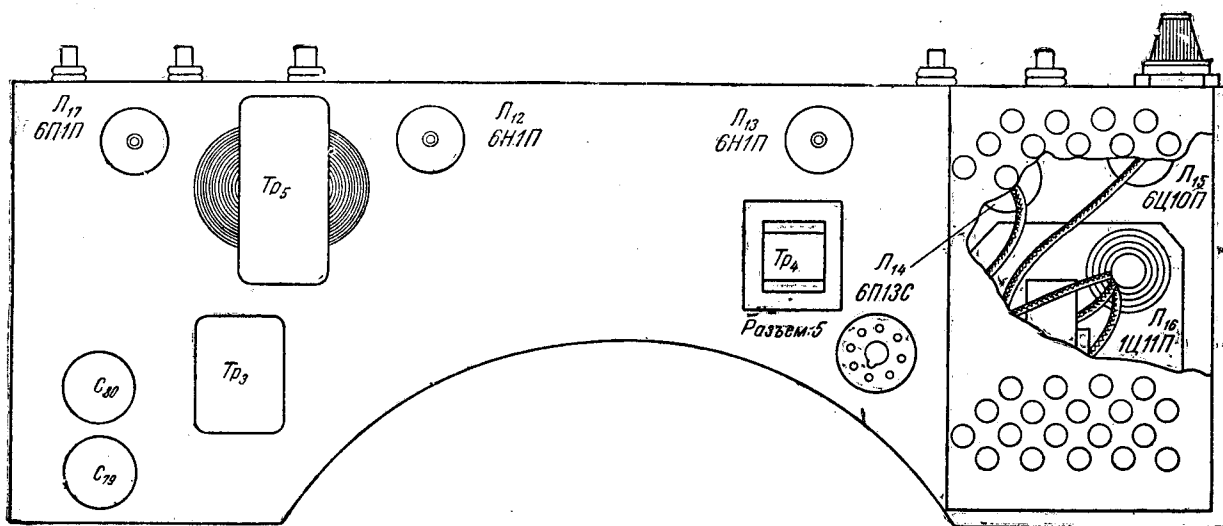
Расположение ламп и деталей на шасси блока развертки (вид сверху).
